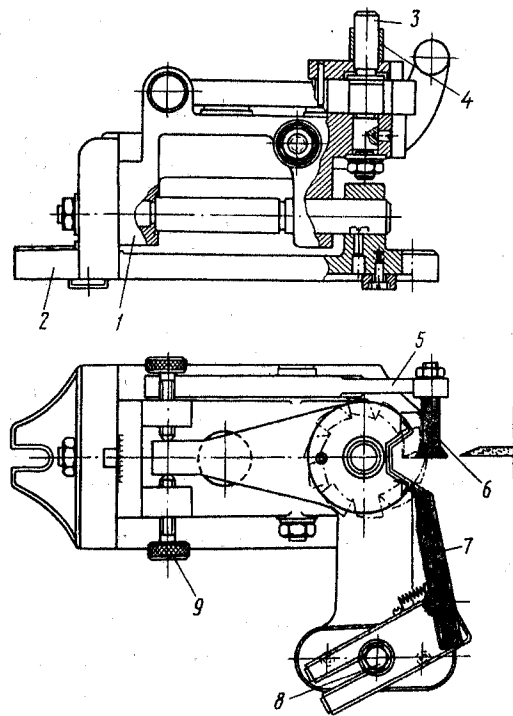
Приспособление для заточки фасонных затылованных фрез по передней поверхности
